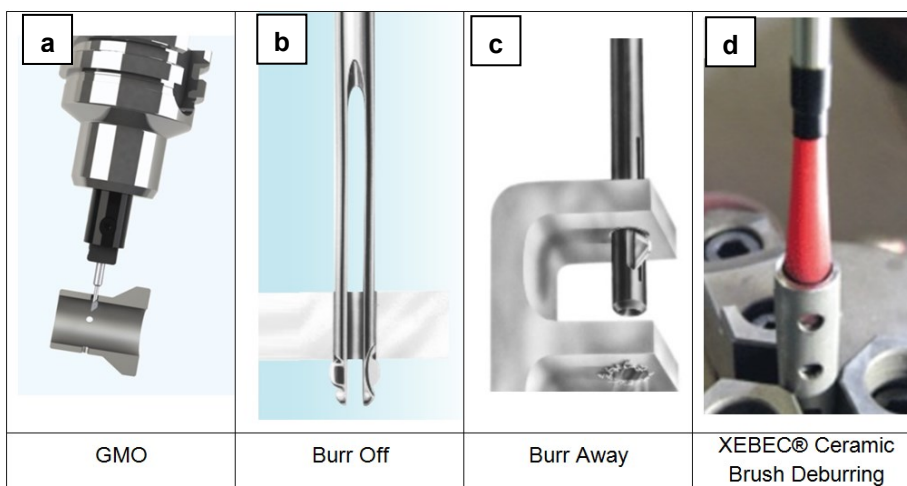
Ausgewählte Werkzeuge für die Entgratversuche
